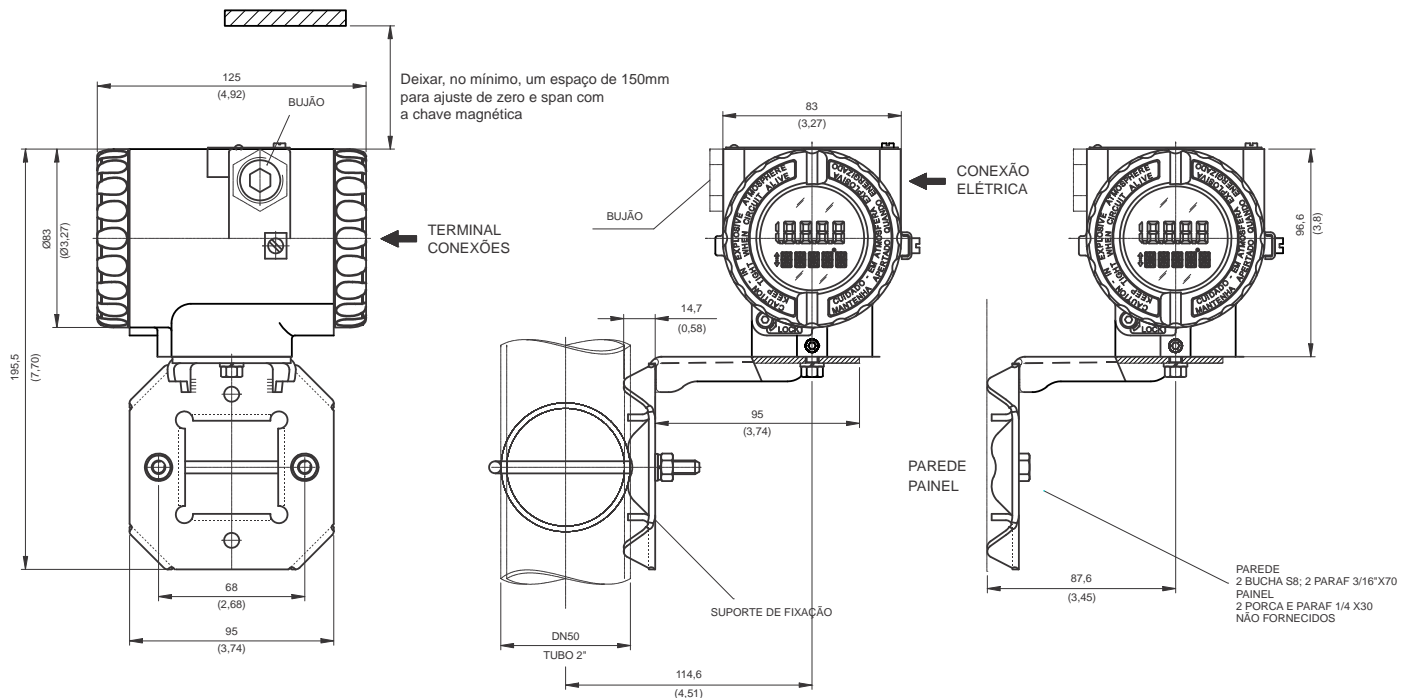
Desenho Dimensional e Posições de Montagem
